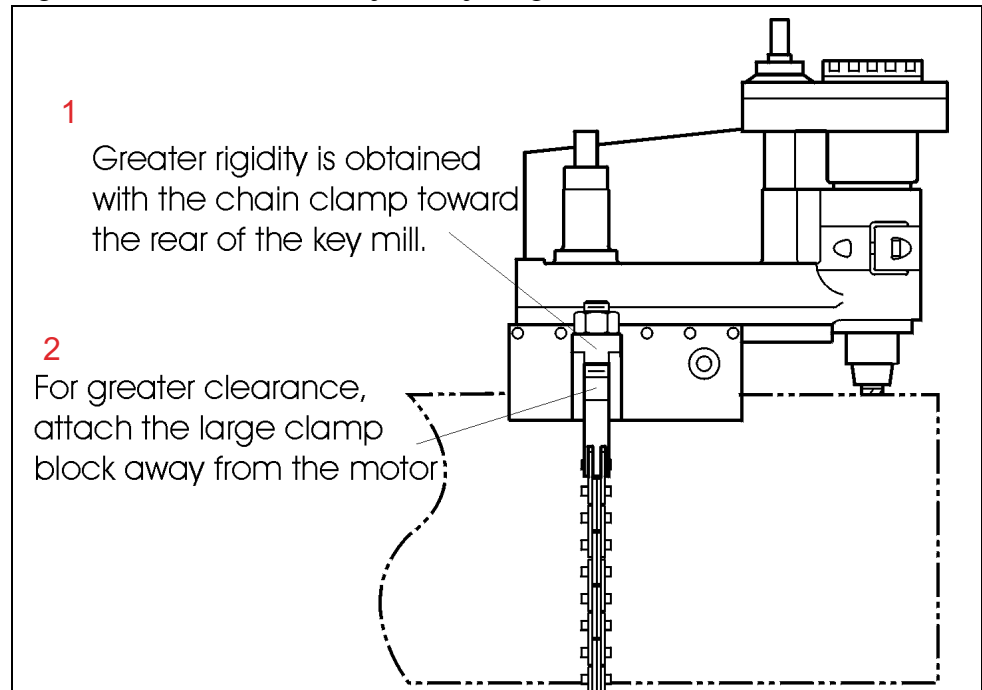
MONTAJE DEL EJE LARGO DE LA KM3000
